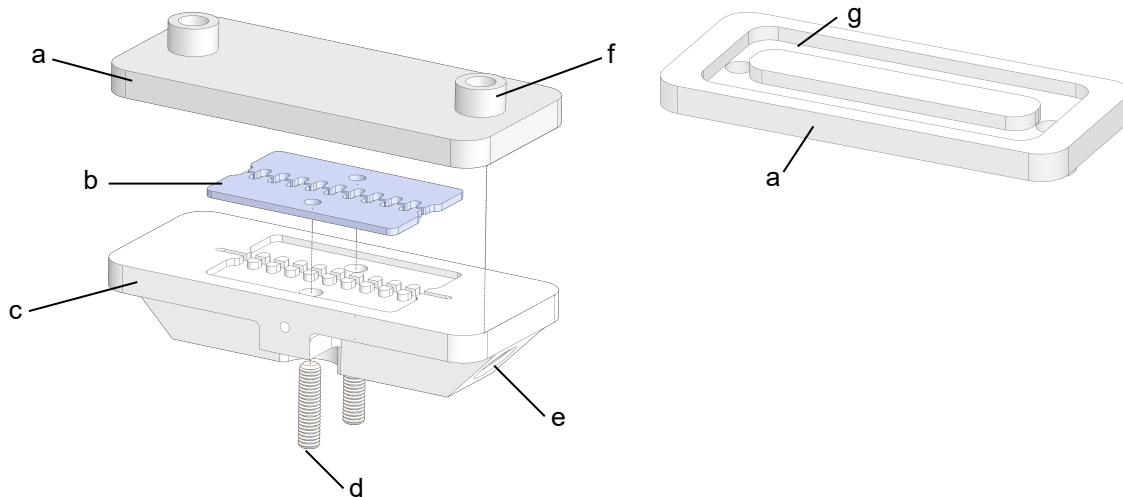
Links: Explosionszeichnung des Kanals: a) Oberteil, b) Elektroden, c) Unterteil, d) Gewindestifte, e) fluidische Anschlüsse, f) Einfüllöffnungen für Harz; rechts: Unteransicht des Oberteils mit g) Hohlraum zum Einfüllen des Harzes
